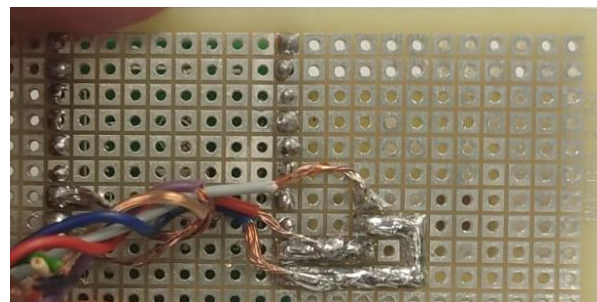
Soldaduras y conexiones segundo prototipo
